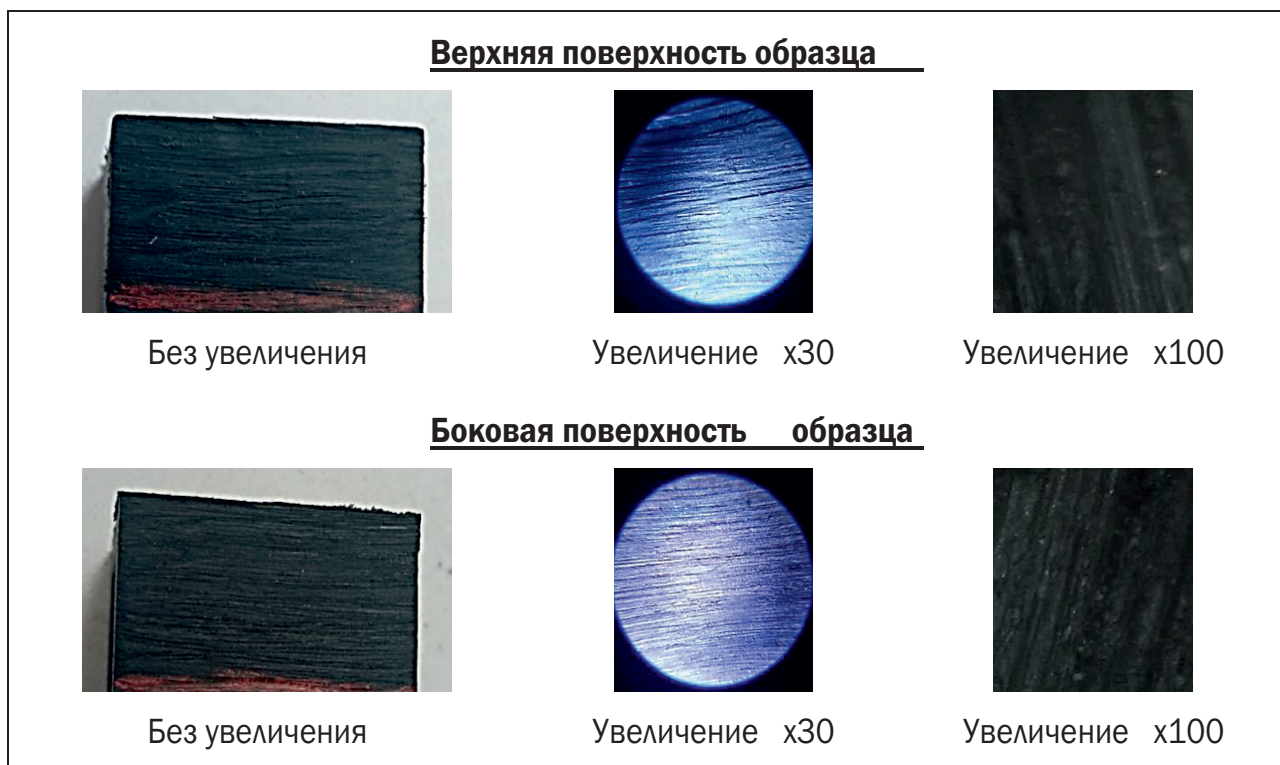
Часть заготовки, обработанная абразивным кругом крупной зернистости
